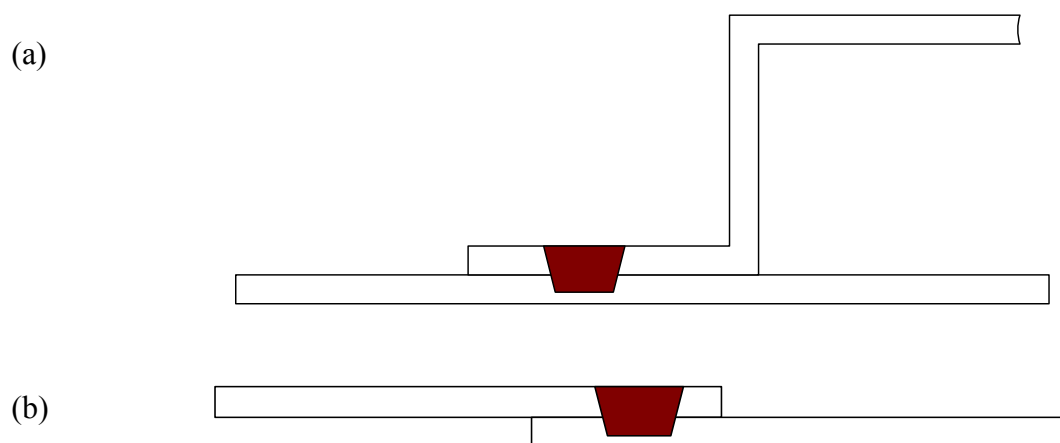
Différents types de joints soudés par recouvrement, (a) soudure entre un raidisseur et une tôle, (b) soudure entre deux plaques.
